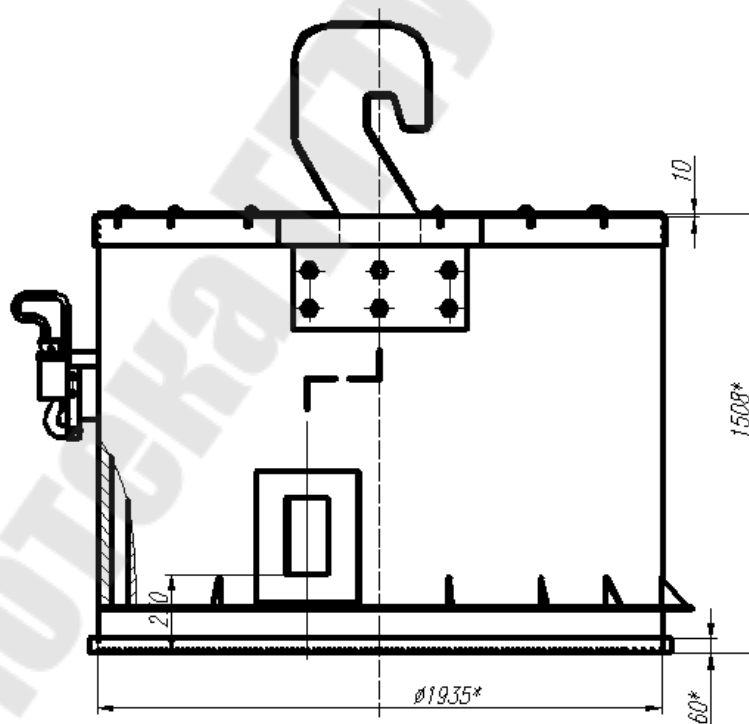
Двухкорпусная бадья, разработанной установки подогрева шихты.
